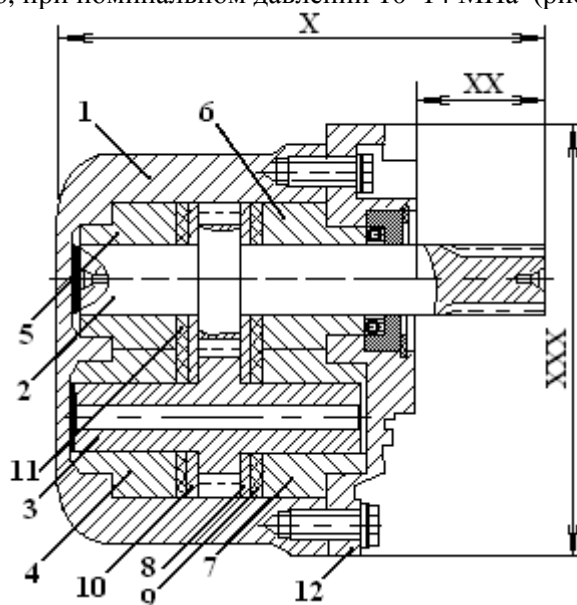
Устройство насоса НШ-У: 1 – корпус; 2 – ведущий вал - шестерня; 3 – ведомый вал - шестерня; 4, 5, 6, 7 – втулки; 8, 10 – компенсаторы; 9, 11 – уплотнения компенсаторов; 12 – крышка
